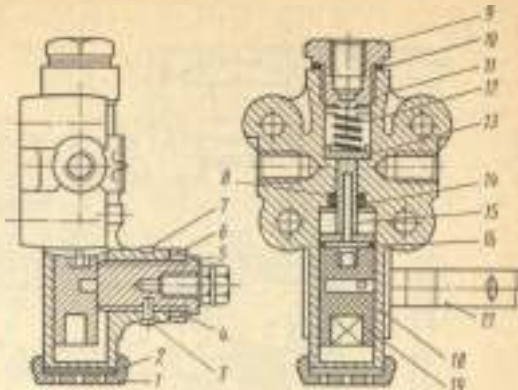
Клапан регулирования уровня пола: 1 — защитный колпак; 2 — войлочная прокладка; 3 — шпонка; 4 — замочное кольцо; 5 — палец привода; 6 — войлочное кольцо; 7 — разжимное кольцо; 8 — опорное кольцо; 9 — редукционный ниппель; 10 — уплотнительное кольцо; 11 — корпус; 12 — нажимная пружина; 13 — тарелка клапана; 14 — сальник; 15 — поршневой палец; 16 — игольчатый ролик; 17 — рычаг управления; 18 — кольцо; 19 — поршень
